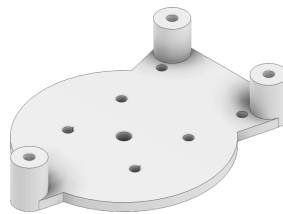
Vista isométrica del soporte para el montaje frontal del sensor FHL-LD20
